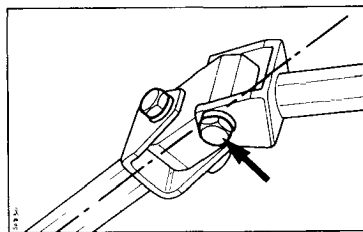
Перед затяжкой болта выровняйте ось промежуточного вала с центром соединительного блока универсального шарнира
